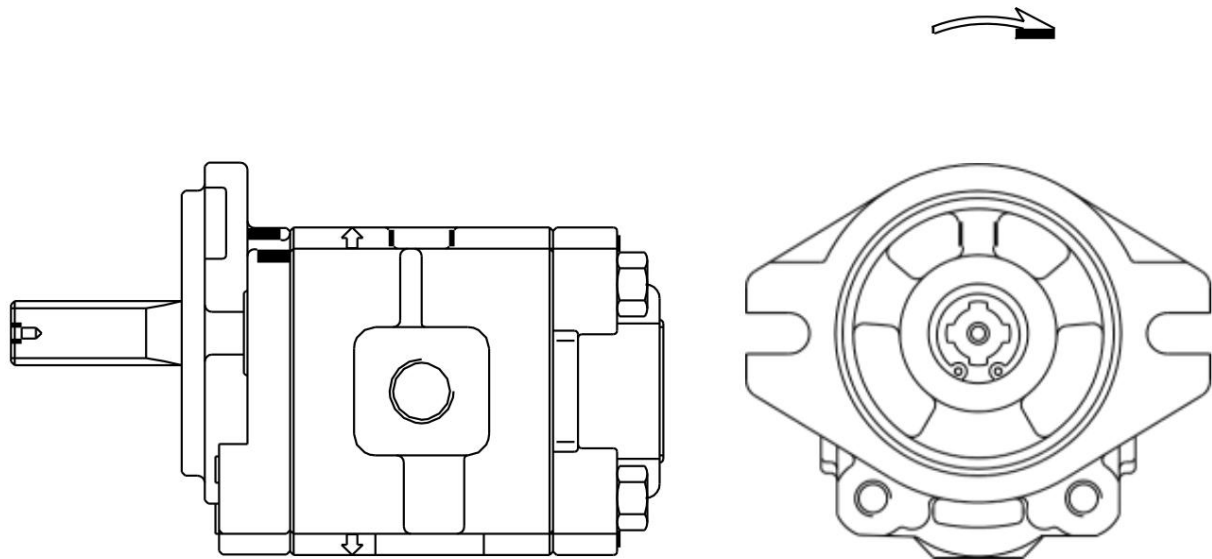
Umrisszeichnung einer Zahnradpumpe
